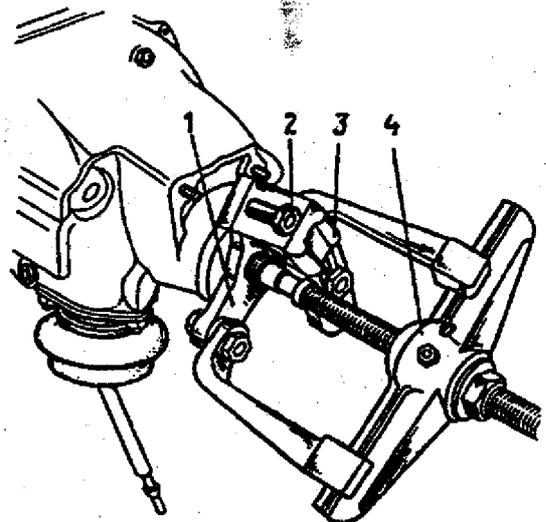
Remoção do flange: 1 - flange do acoplamento elástico; 2 - parafusos de fixação do dispositivo ao flange; 3 - placa do extrator A.40005/3; 4 - extrator A.40005/3.
